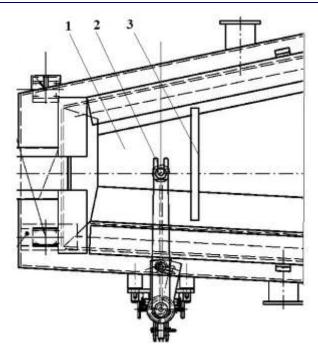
Конструкции оборудования разливочной камеры ковша МНЛЗ:
